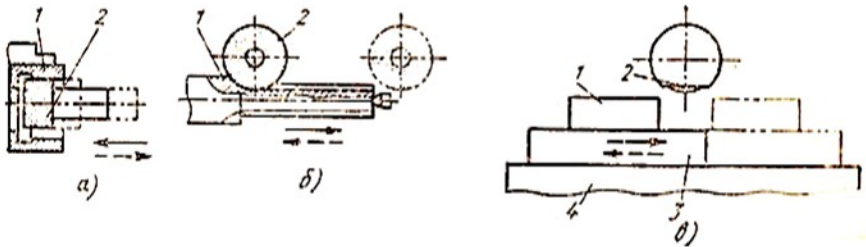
Схемы положения инструмента относительно детали при реверсе стола на шлифовальных станках.
